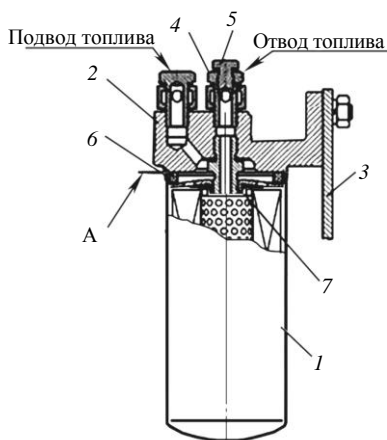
Замена неразборного фильтра тонкой очистки топлива: 1 – фильтр; 2 – корпус; 3 – кронштейн; 4, 7 – штуцера; 5 – пробка для выпуска воздуха; 6 – прокладка
